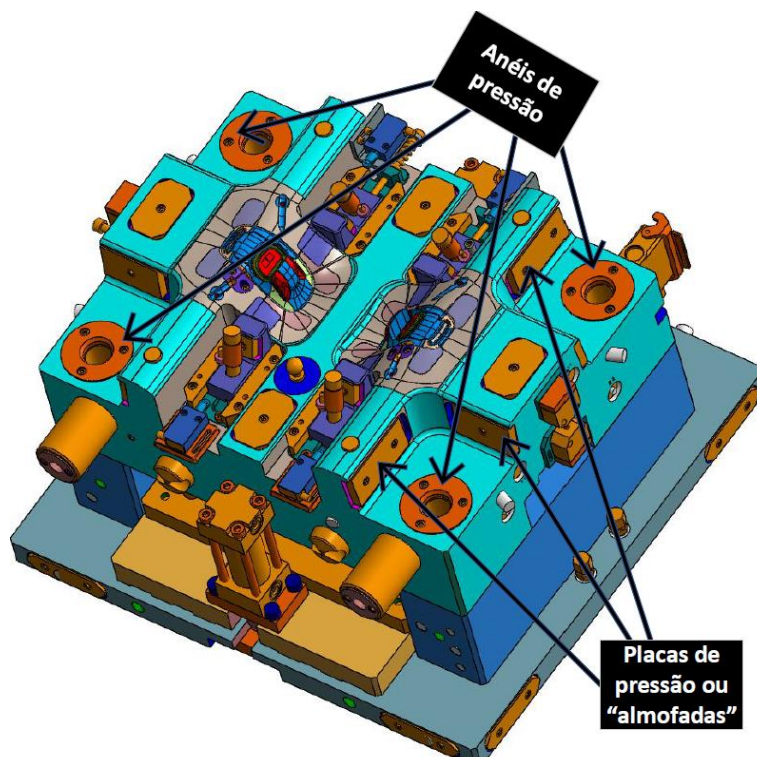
Vista isométrica para as "almofadas" do molde (Lado 2)
